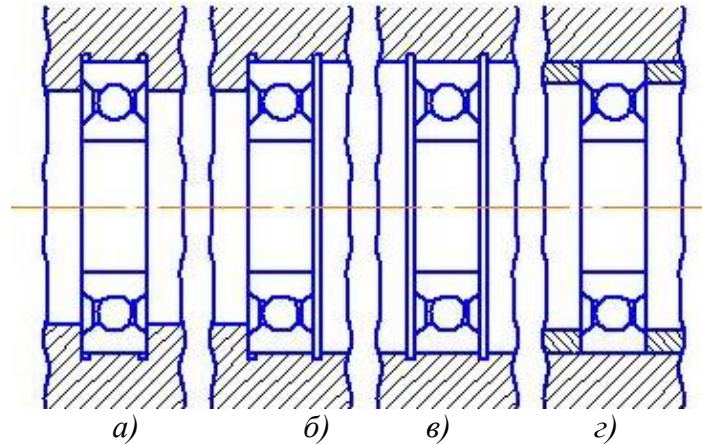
Підвищення технологічності обробки корпусу підшипника
